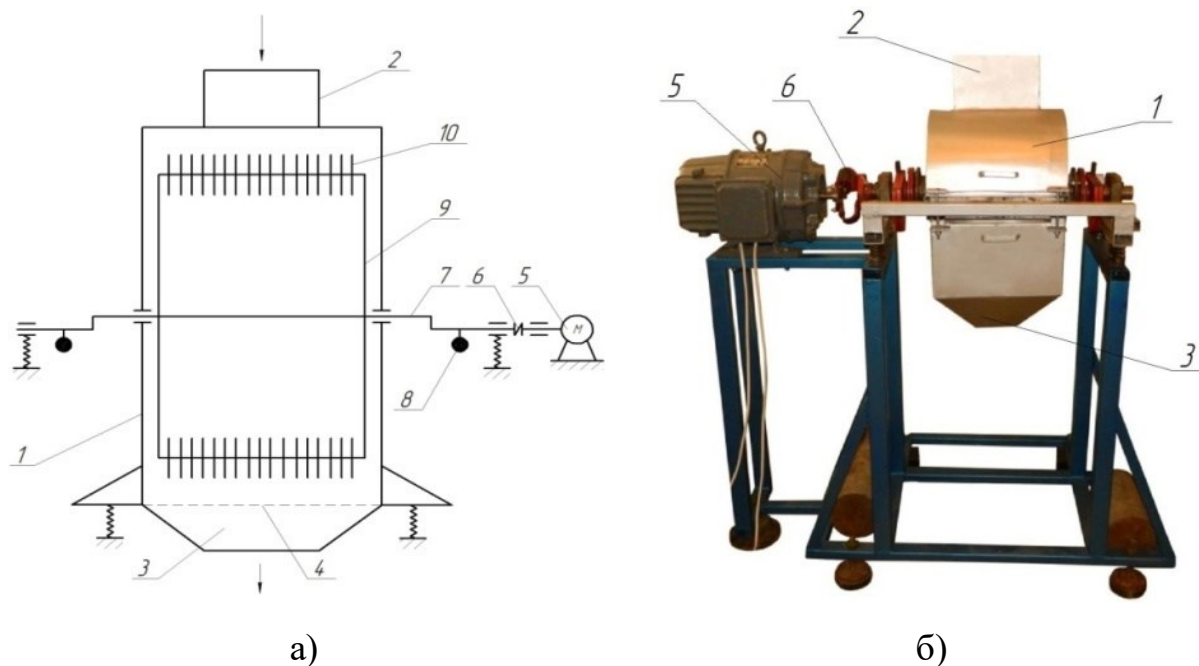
Вібраційна дискова дробарка: а) – принципова схема; б) – загальний вигляд; 1 – корпус; 2, 3 – завантажувальна та розвантажувальна горловина; 4 – сито; 5 – електродвигун; 6 – муфта еластична; 7 – вал кінематичний; 8 – противаги; 9 – ротор; 10 – біла дискового-типу
